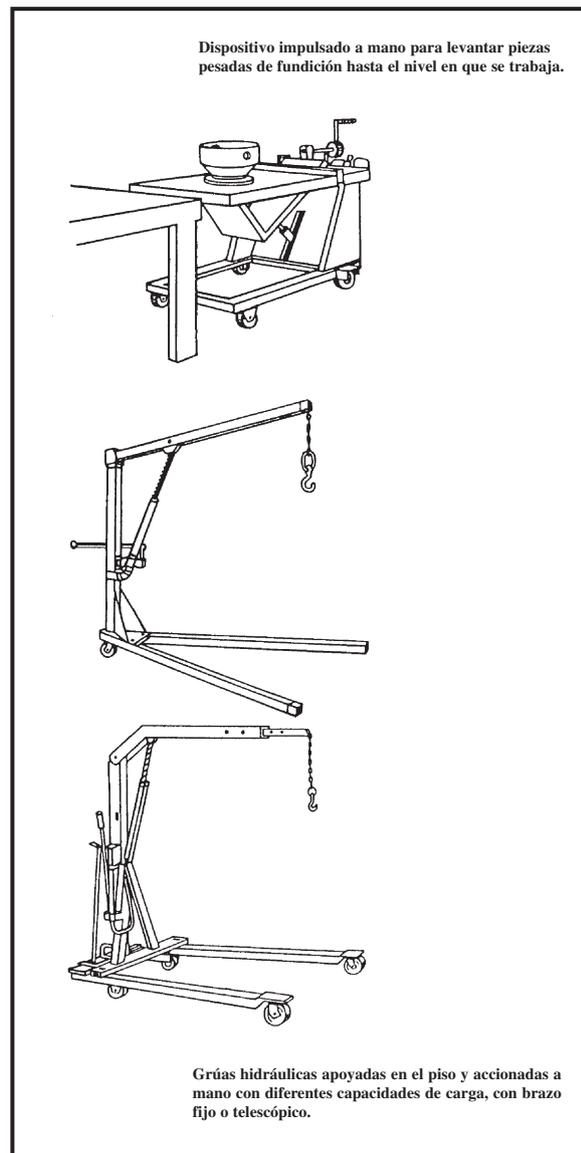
Equipos utilizados para el levantamiento y transporte de cargas seguro y sin esfuerzos.
